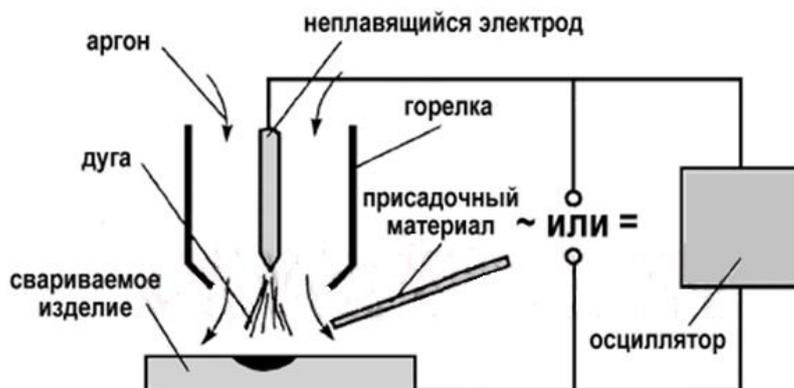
Сущность аргонодуговой сварки неплавящимся электродом
